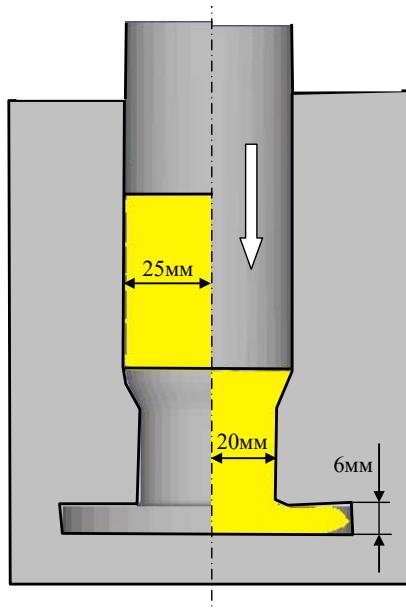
Схема процесу радіального видавлювання суміщеного з попереднім редукуванням заготовки
